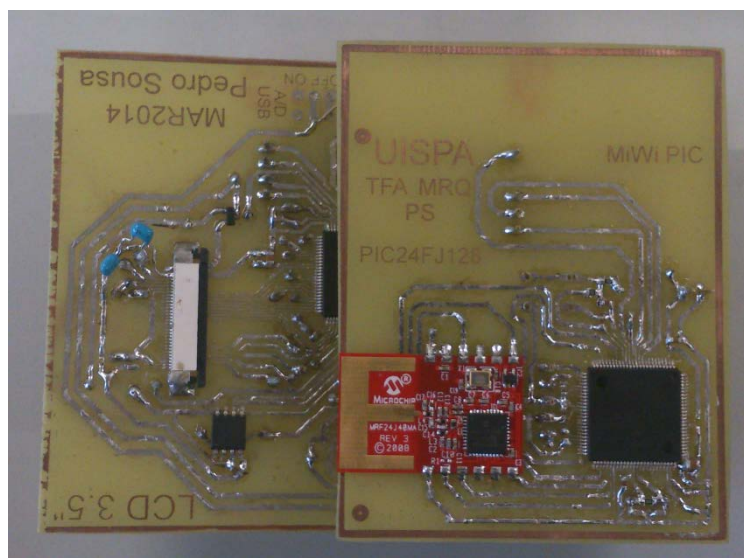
Fotografia da ligação entre a PCB central e a PCB MiWi
